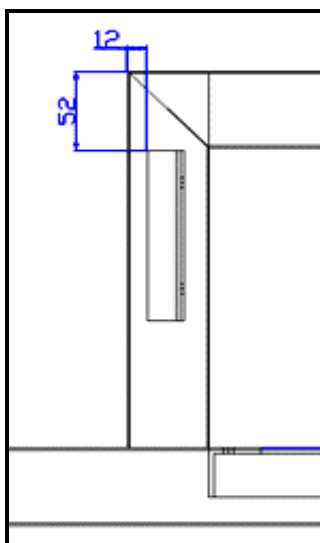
Posição das cantoneiras superiores. (detalhe 1)
